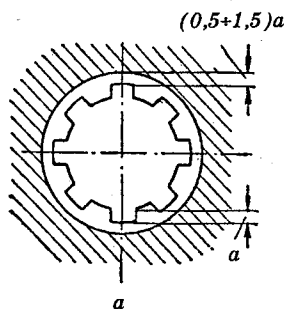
Ремонт шлицевого отверстия постановкой кольца:
